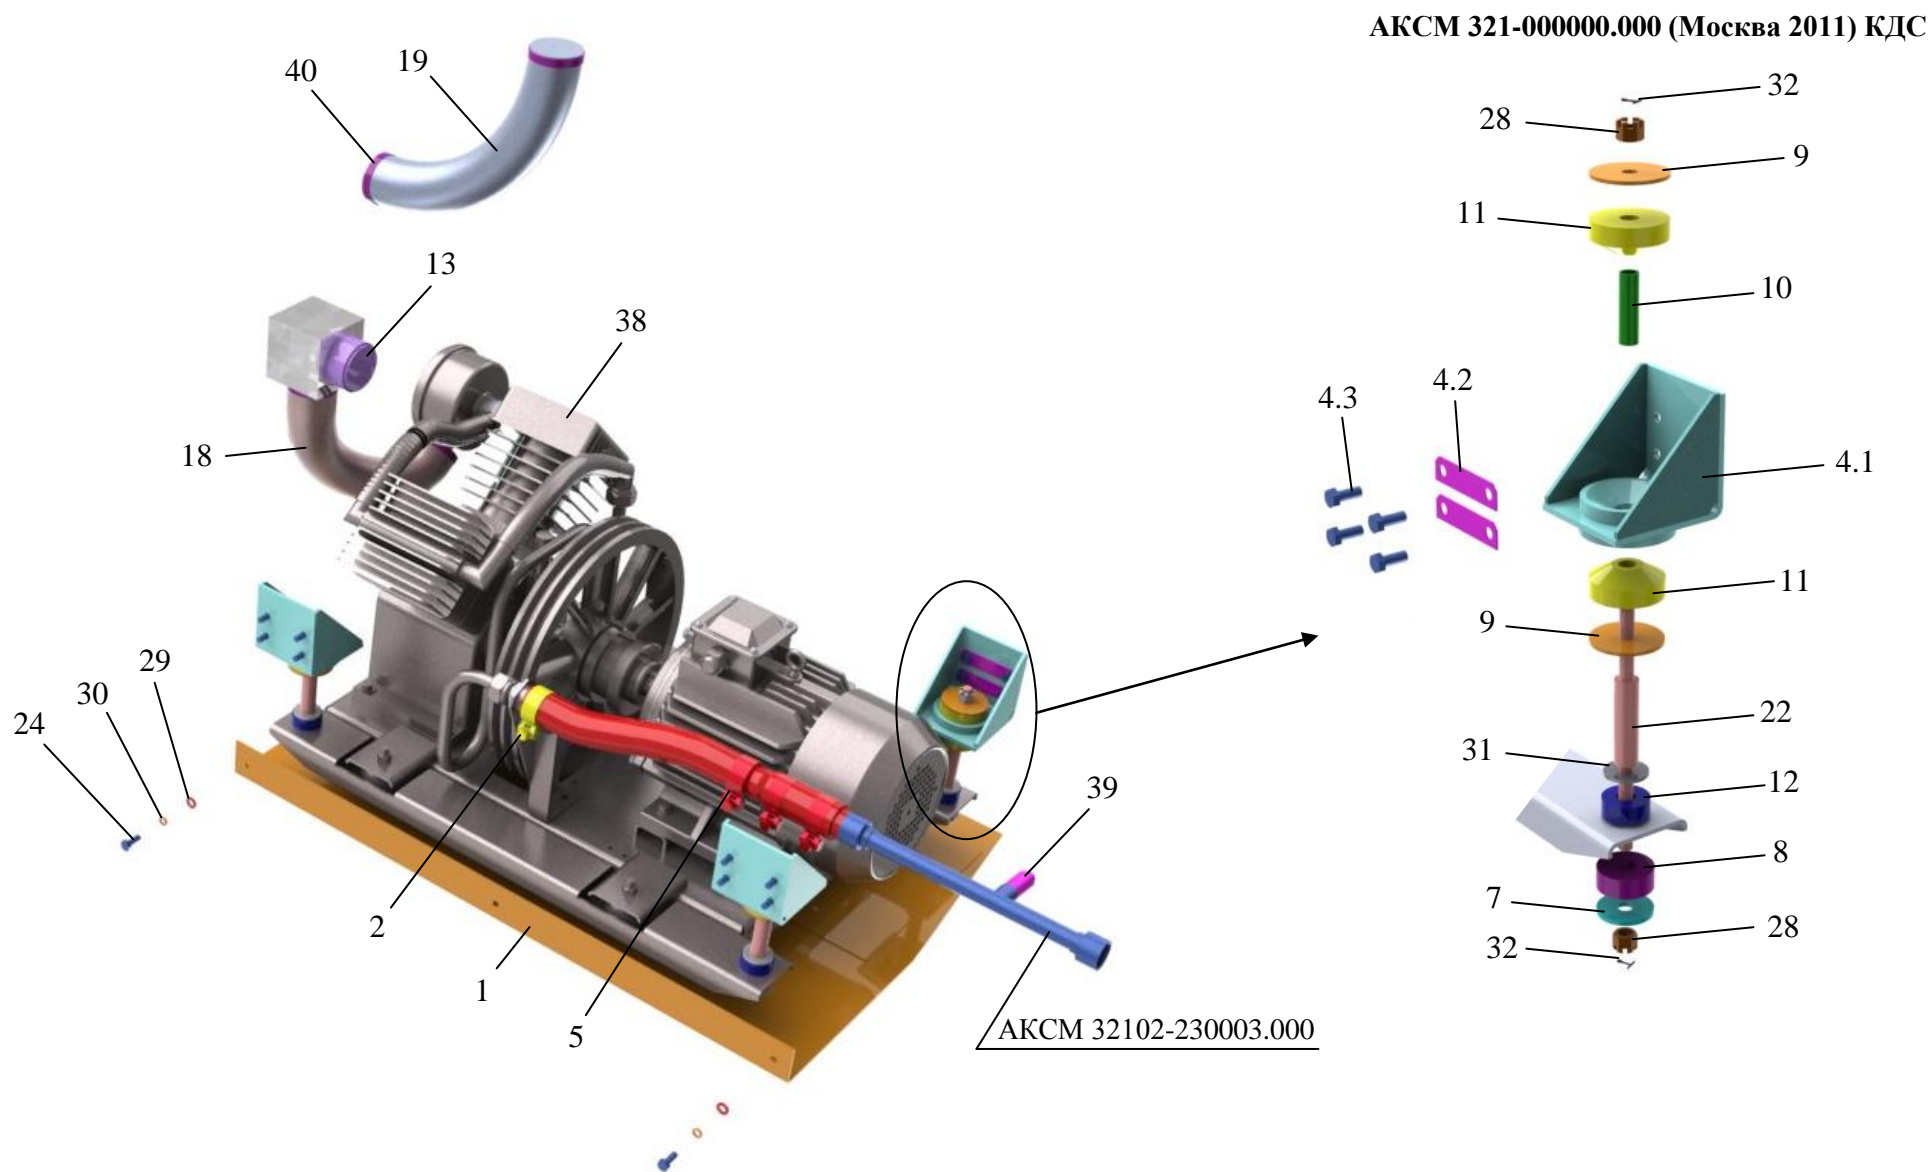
Установка компрессора АКСМ 333-232300.000
